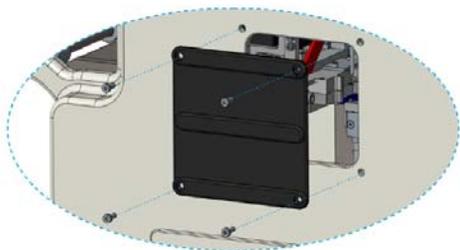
Retrait du panneau pour révéler le guide magnétique de film
